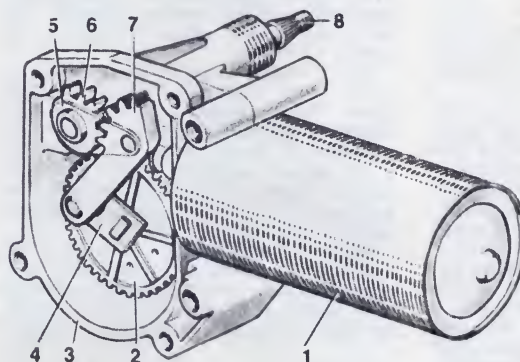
Моторедуктор однощеточного стеклоочистителя: 1 — электродвигатель; 2 — червячная шестерня; 3 — корпус; 4 — кривошип; 5 — серьга; 6 — зубчатый сектор; 7 — шатун; 8 — выходной вал.
